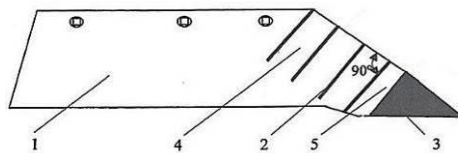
Леміш з армованим долотом і напавленою частиною, що заглиблює: 1 – леміш; 2 – армуючий валик; 3 – область напавлення; 4 – носок; 5 – заглиблююча частина
